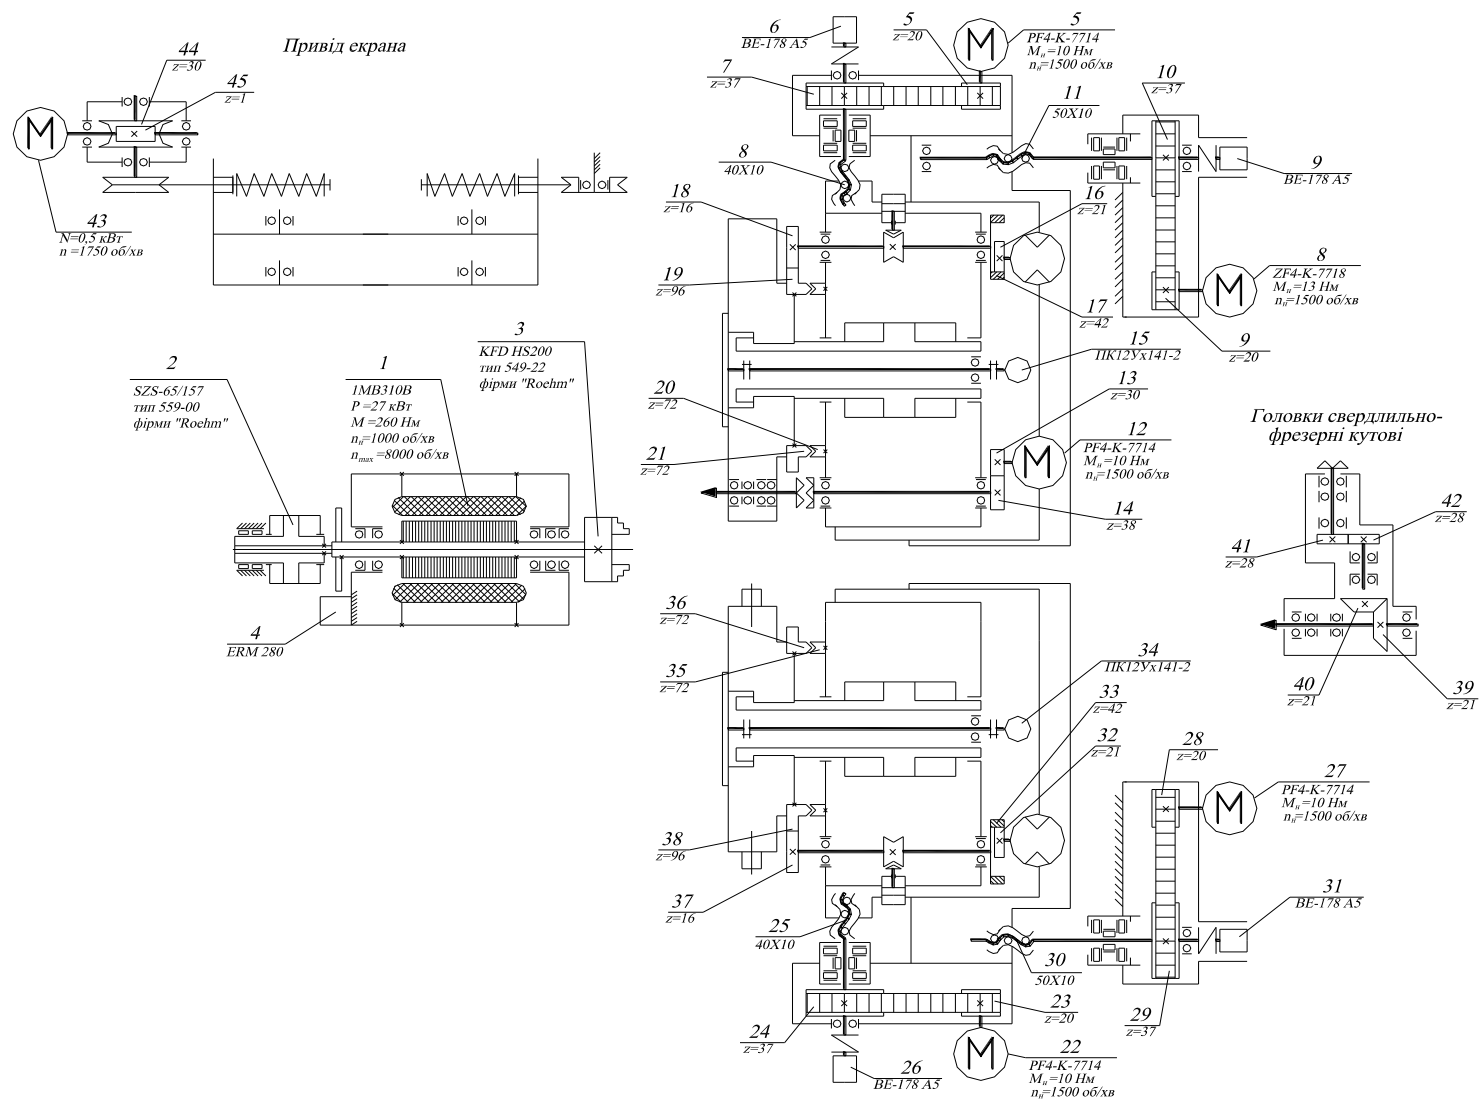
Кінематична схема двосупортного токарного верстату з ЧПК для реалізації дволезової обробки консольно-закріплених циліндричних деталей
